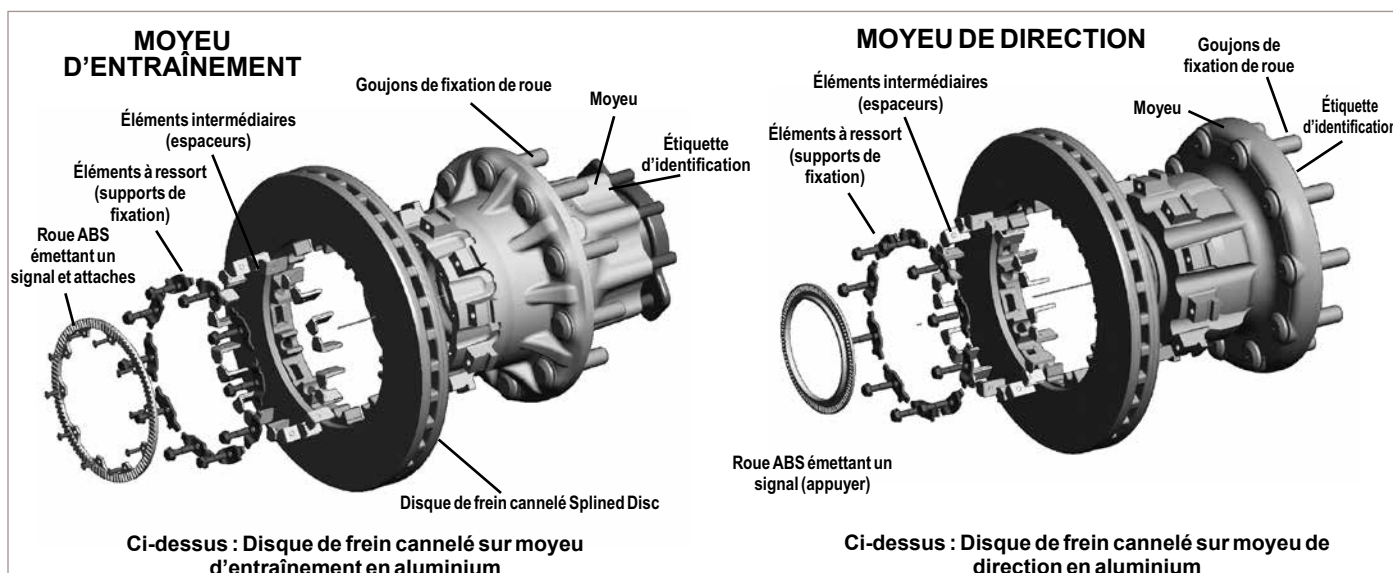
EXEMPLES DISQUE DE FREIN CANNELÉ - VUES EXPLOSÉES
